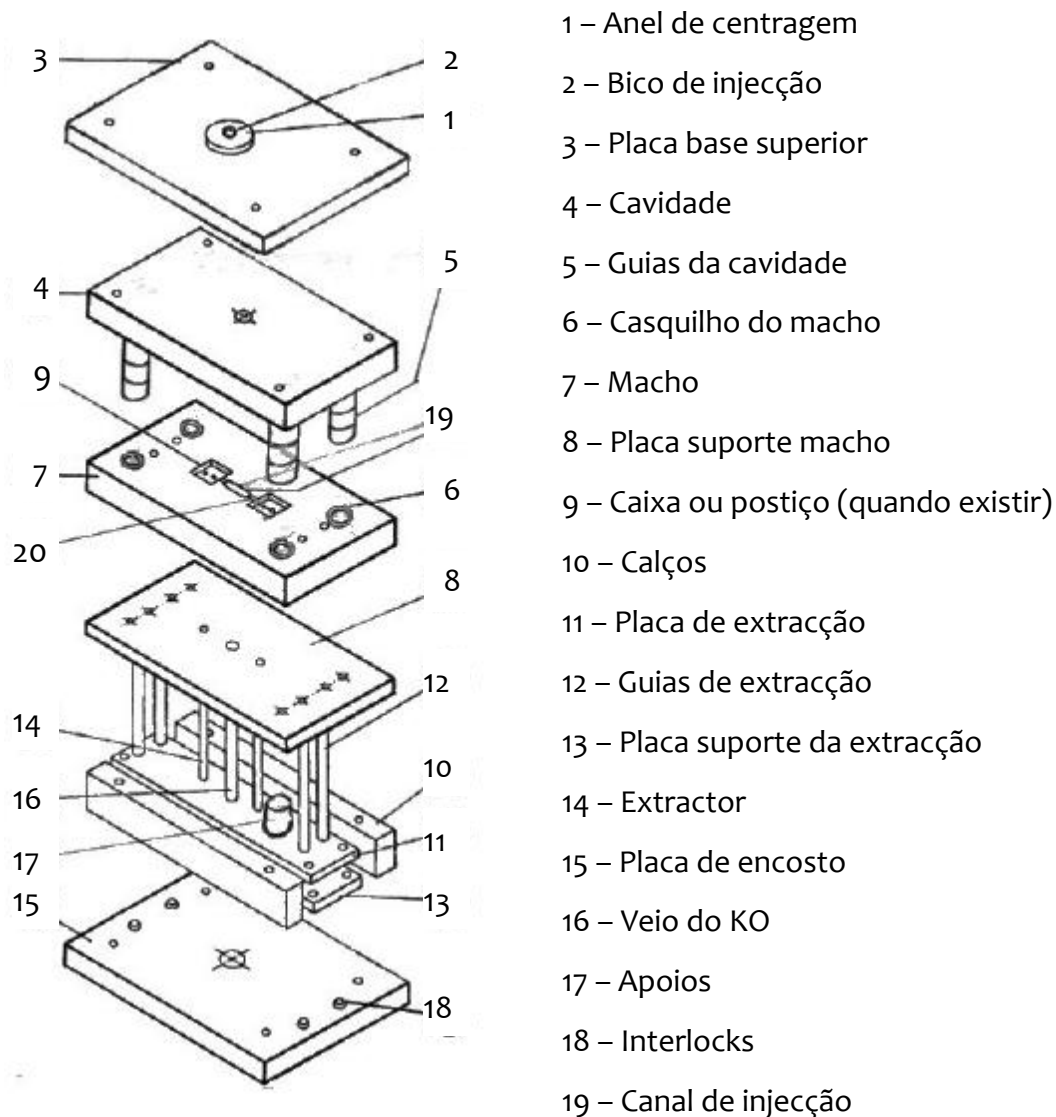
Desenho esquemático pormenorizado de um molde de duas placas. [3]
